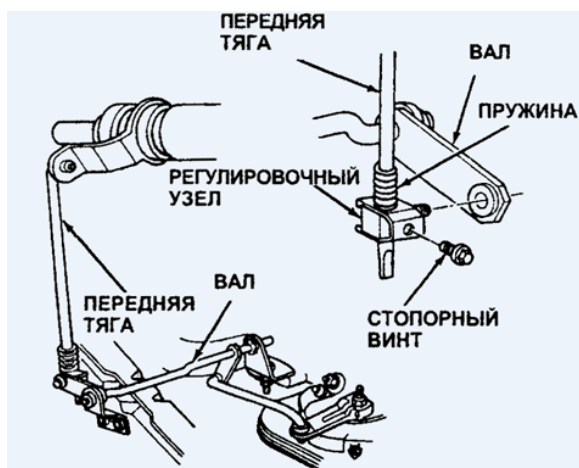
Детали механизма переключения режимов коробки передач
